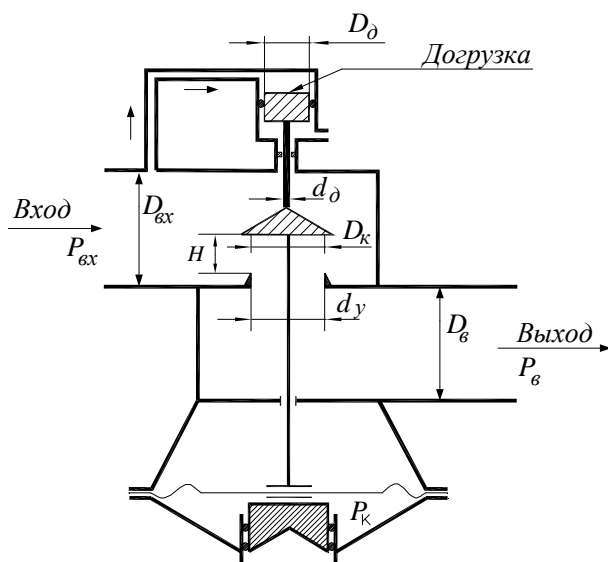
Усовершенствованный стандартный редуктор с «догрузкой»
